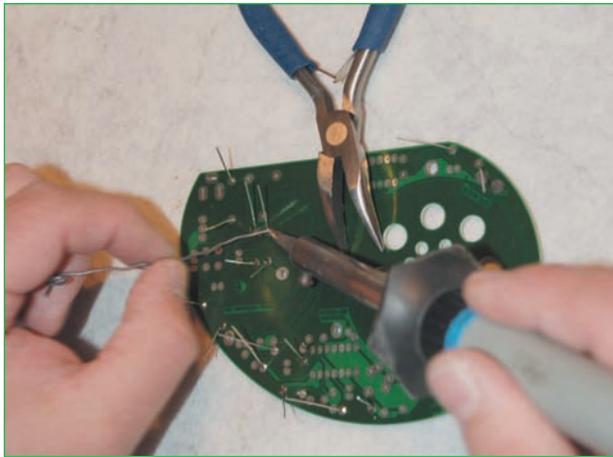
Nachdem Sie alle Widerstände laut Bestückungsplan eingesteckt haben, löten Sie die Drahtanschlüsse auf der Rückseite der Platine an.
